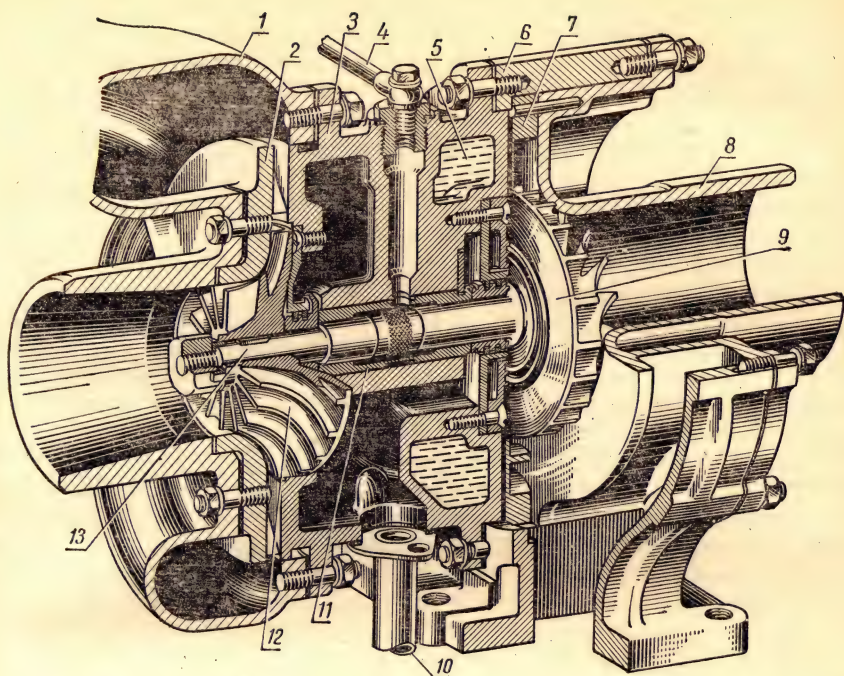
Турбокомпрессор (СМД-ТКР-41Н), устанавливаемый на двигатели СМД-17К и СМД-18К:
